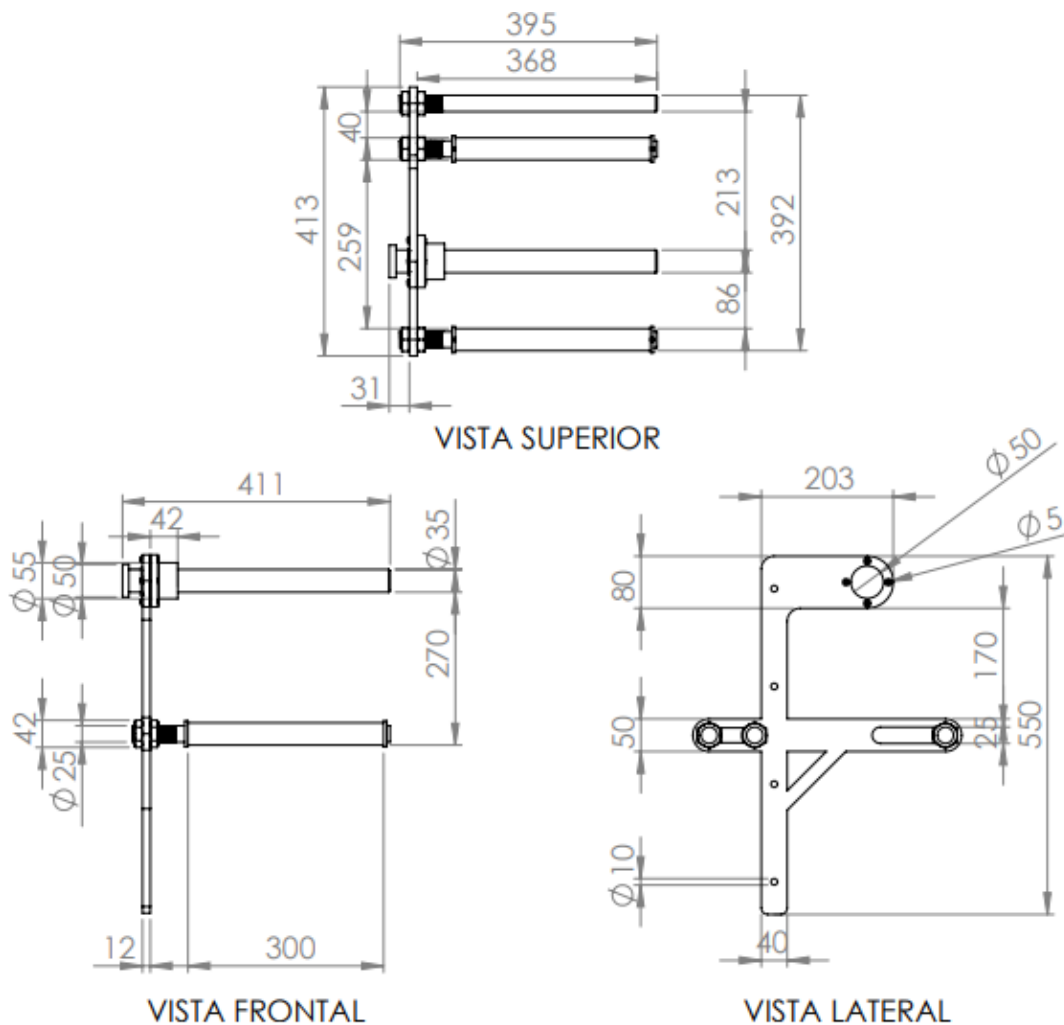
Dimensiones del sistema des embobinador en milímetros (elaboración propia).
